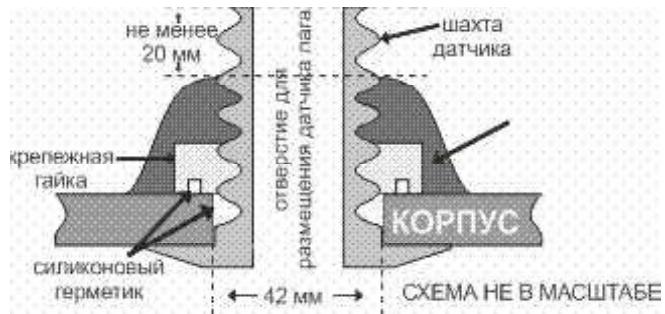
Установка шахты датчика лага (вид в разрезе).
